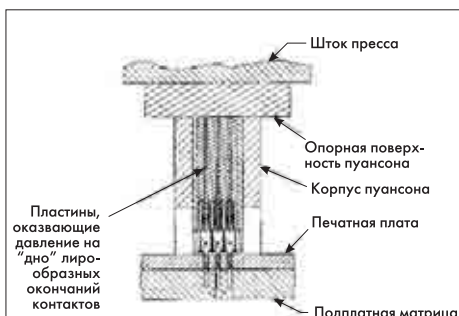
Поперечное сечение пуансона для запрессовки розеточных соединителей
